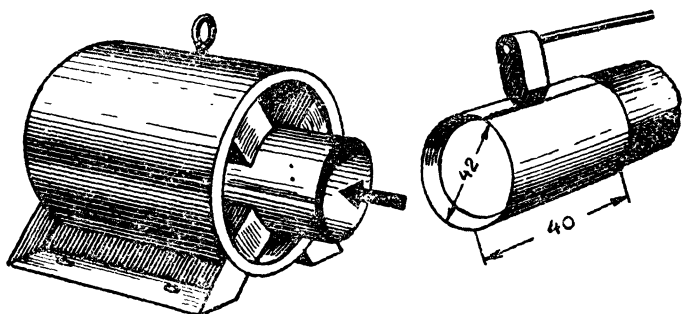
Вдвиньте внутрь статора заготовленную трубку.
